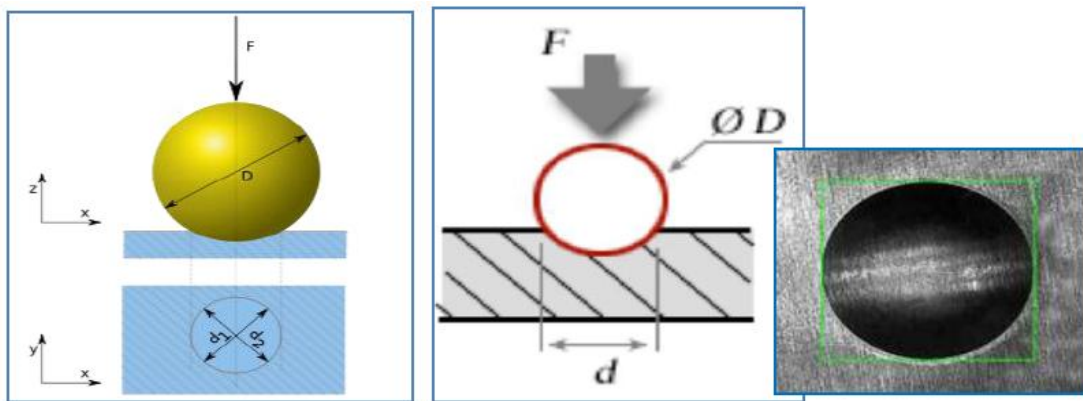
Principe de l'essai Brinell et empreinte typique de l'essai
